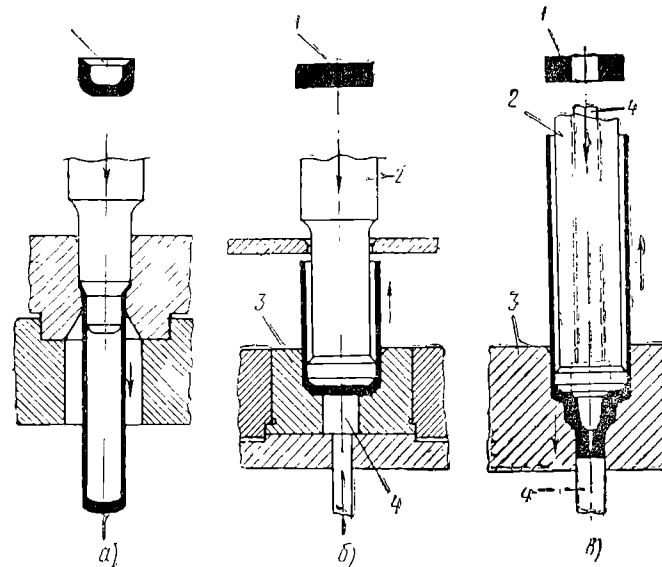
Холодная объемная штамповка выдавливанием: а — прямым, б — обратным, в — комбинированным; 1 — заготовка, пуансон, 2 — матрица, 4 — выталкиватель, 5 — съёмник (стрелками показано направление течения металла)
